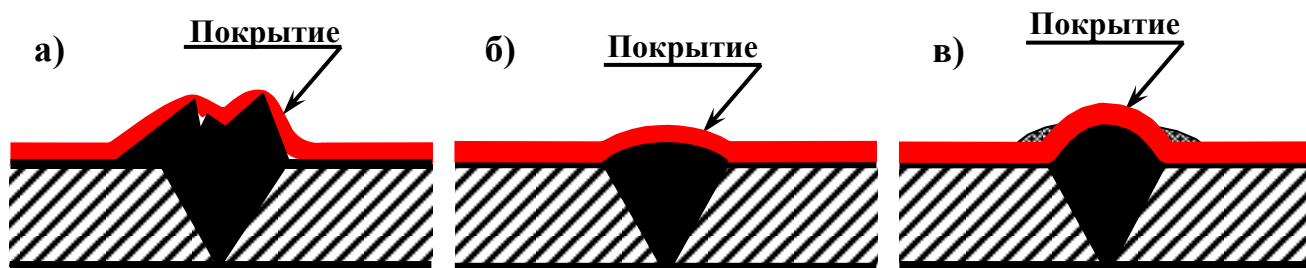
Распределение пленки покрытия по поверхности сварных швов:
